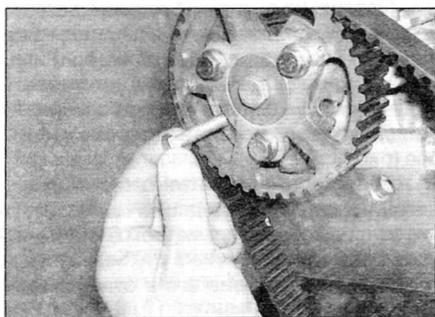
Пропустите болт/сверло через отверстие в ступице зубчатого шкива распределительного вала и вставьте его в головку цилиндров (двигатели 2.0 л)
